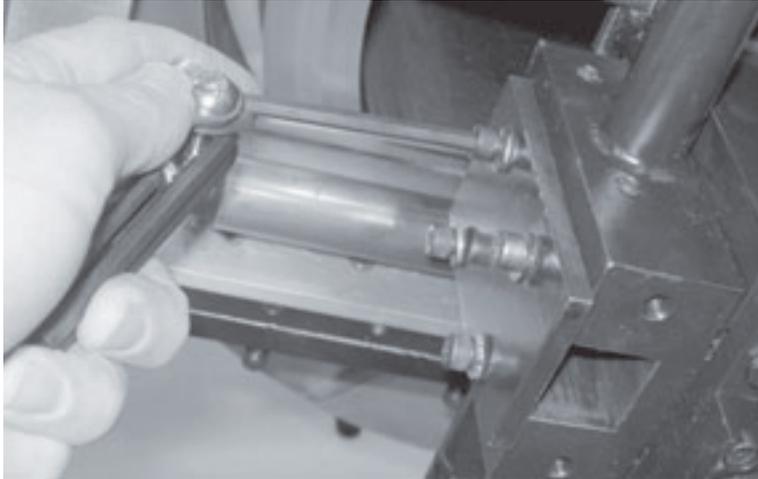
Ziehen Sie den Auslösebolzen heraus, um den Auslöser für die Innenbearbeitung auszukuppeln.
